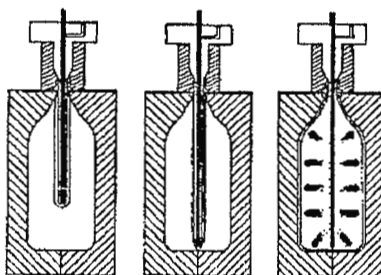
Moldeo por soplado y expansión (Inyección dilatada)
